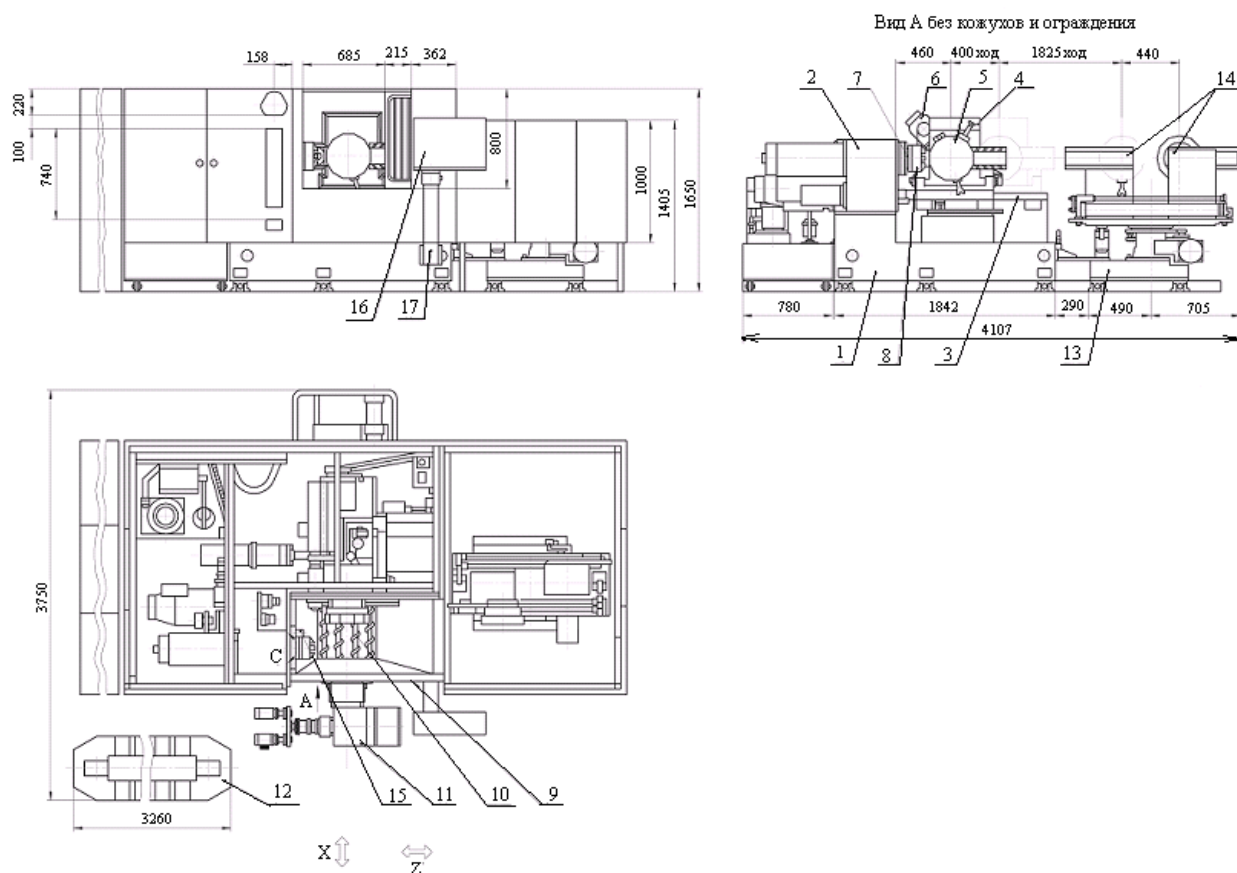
Компоновочная схема РТК на базе многоцелевого станка ИРТ180ПМФ4
